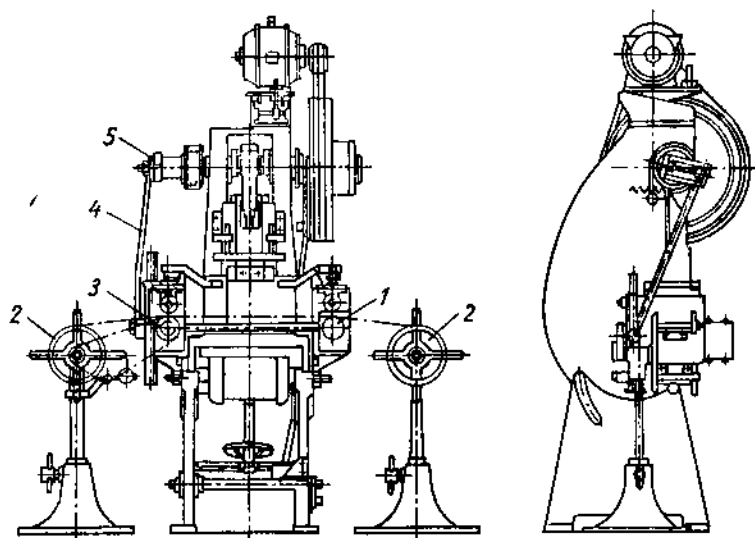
Схема двухстоечного наклоняемого пресса с двойной валковой подачей
